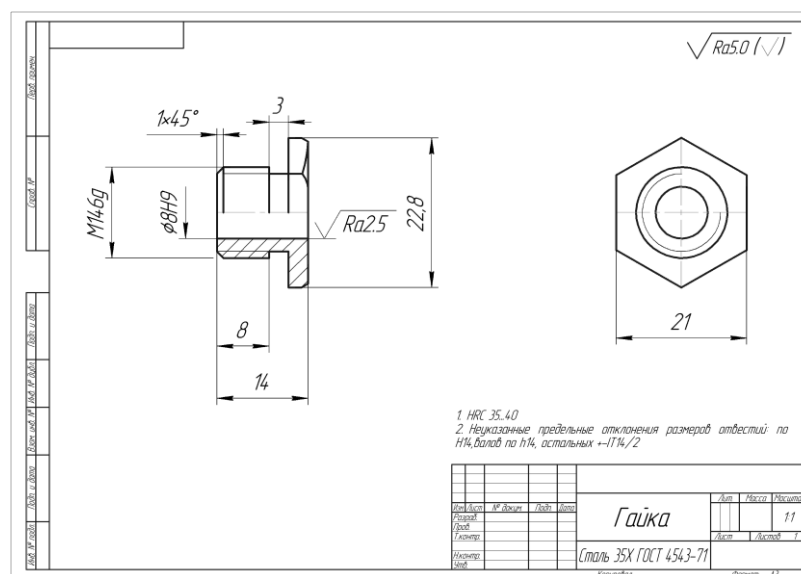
Окончательный вариант рабочего чертежа детали «Гайка»
